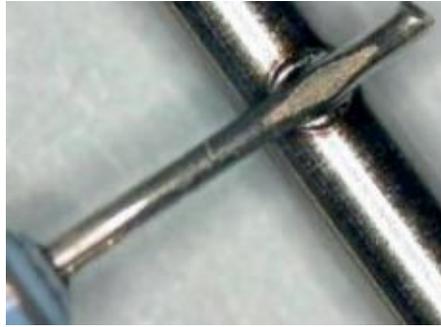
A - Schweißkopf mit geringer Kraft (ehemals MFP60)
